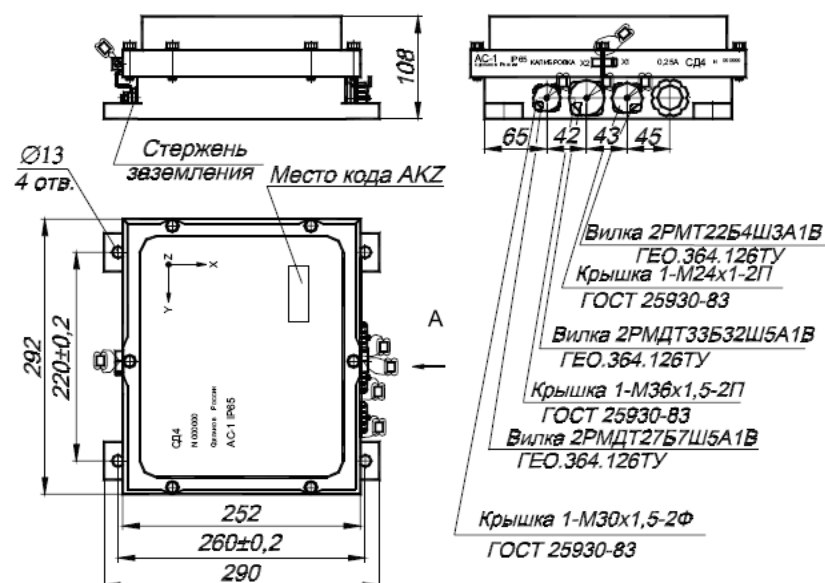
Габаритно-установочные размеры сейсмодатчика
